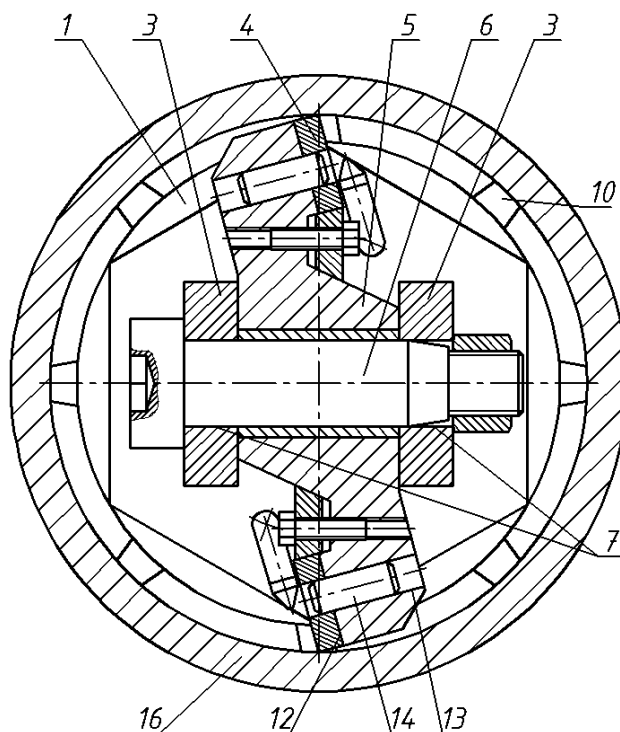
Схема дворізцевої адаптивної розточної головки
